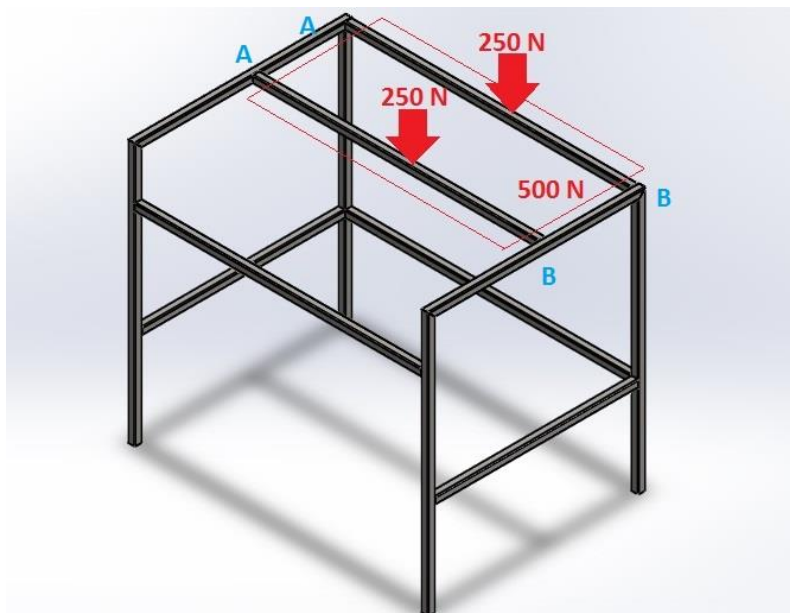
Distribución de la carga 1 en las vigas A-B
